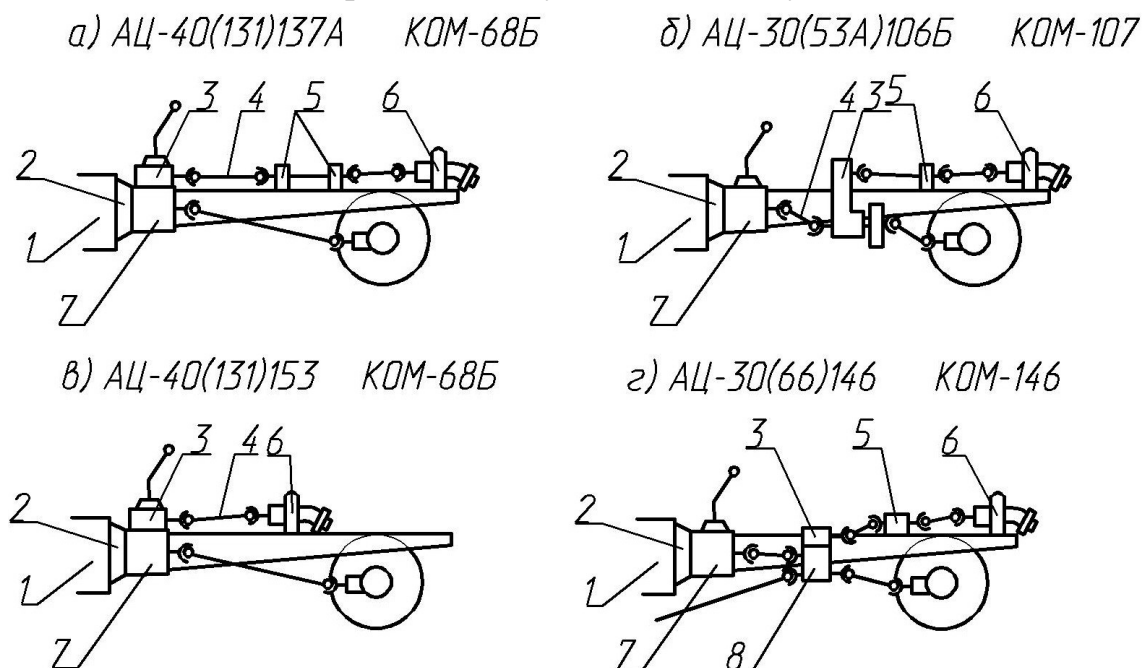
Типовые схемы дополнительных трансмиссий: 1 – двигатель; 2 – сцепление; 3 – коробка отбора мощности; 4 – карданный вал; 5 – промежуточная опора; 6 – пожарный насос; 7 – коробка перемены передач; 8 – раздаточная коробка.
